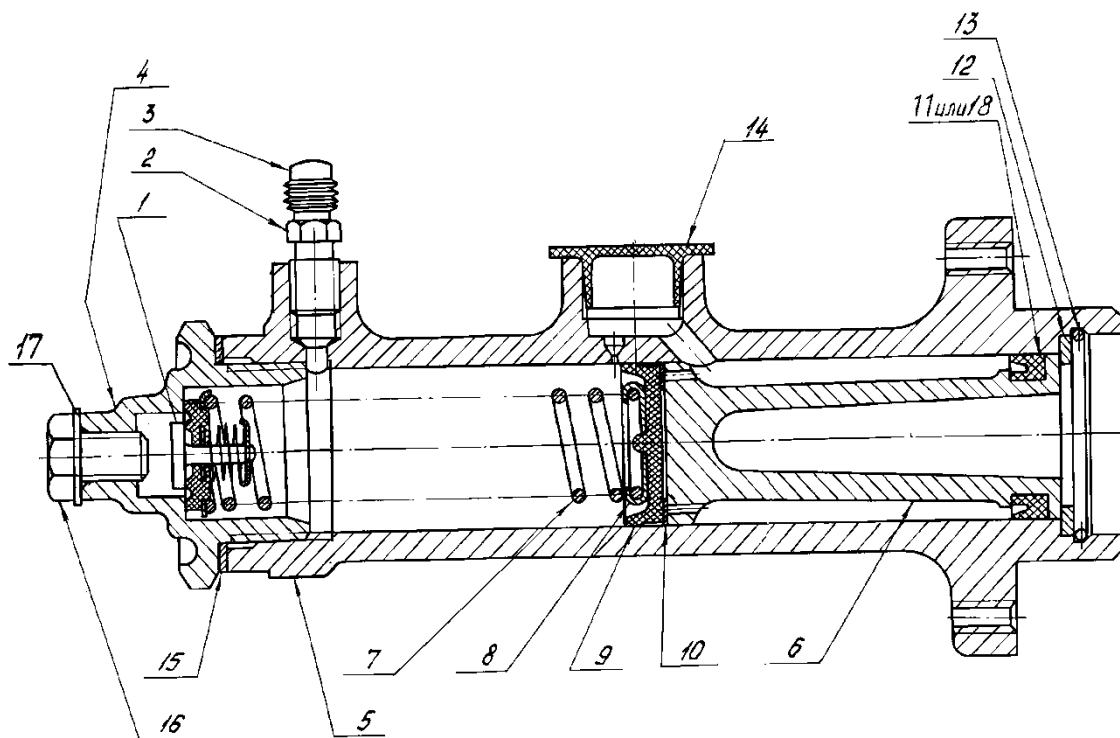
Цилиндр главного тормоза в сборе
